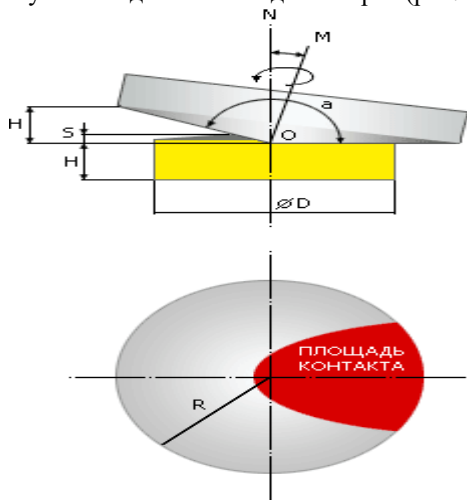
Схема технологии торцевого раскатывания:  $N$  – угол крепления инструмента;  $M$  – угол крепления заготовки;  $a$  – угол профилирования;  $O$  – цент соприкосновения инструмента и заготовки;  $T$  – высота профилирования заготовки;  $S$  – глубина смятия заготовки в инструмент;  $H$  – высота инструмента;  $D$  – диаметр инструмента;  $R$  – радиус заготовки
